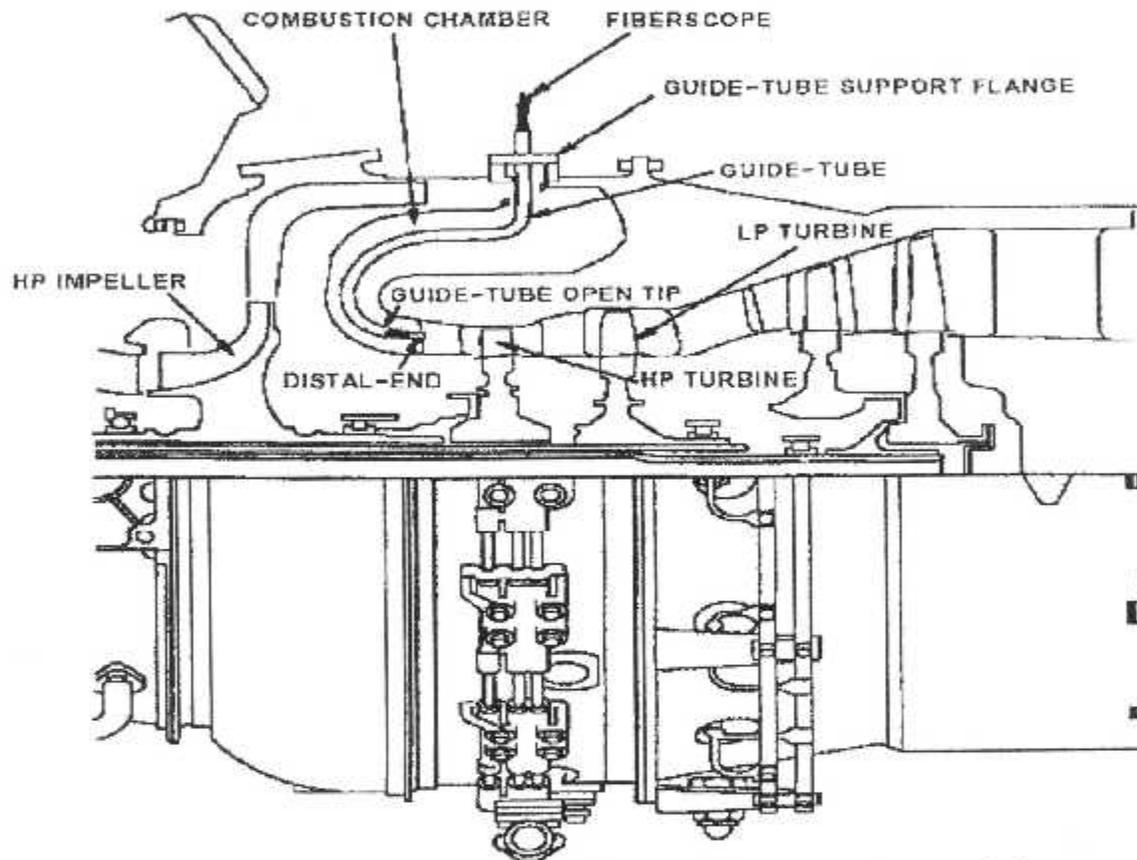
Inspection d'assemblage enveloppe de la chambre de combustion.
